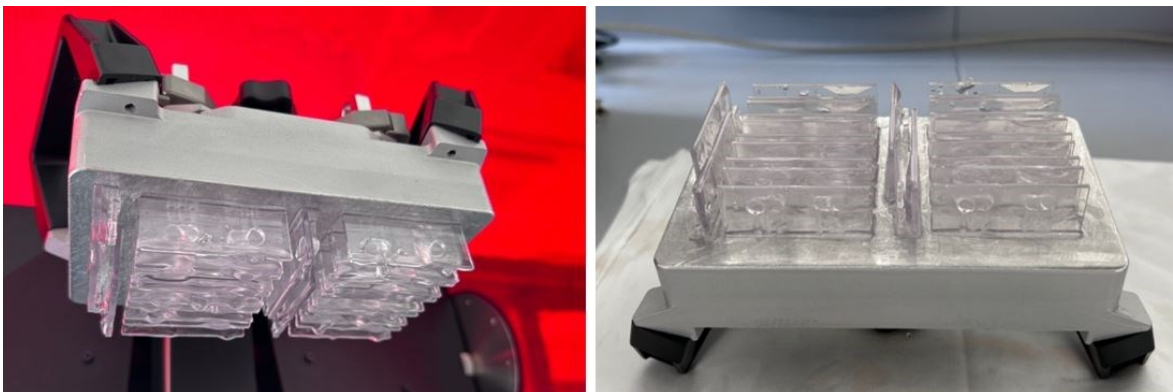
Basisplatten mit Einzelhaken längsseitig auf der Druckplattform
